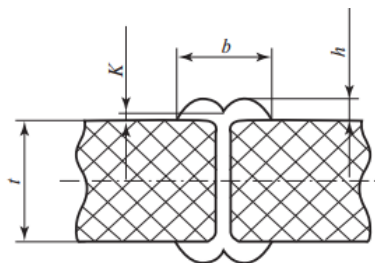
Основные геометрические размеры соединения встык труб из полиэтилена:  $t$  – толщина стенки трубы;  $b$  – ширина шва сварного соединения;  $h$  – высота шва сварного соединения;  $K$  – глубина впадины между валиками грата
